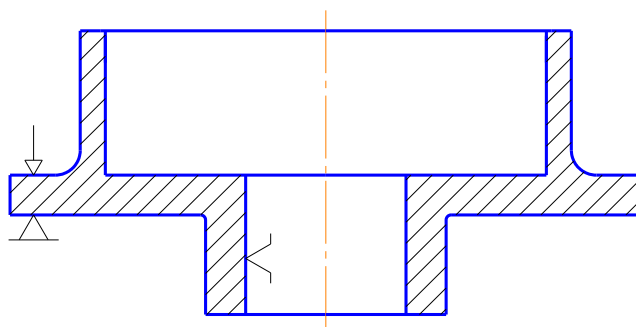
Умовна схема базування деталі на свердлильній операції
